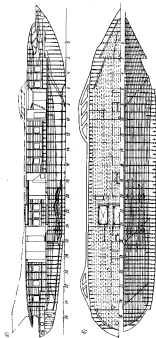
Конструктивная схема корпуса и надстройки телескопа «Спрут»: а — продольный разрез по ДП, б — план главной палубы и донца.
